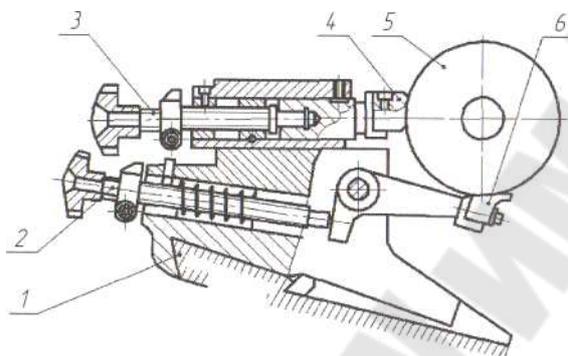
Люнет круглошлифовального станка: 1 – стол; 2,3 – винты; 4, 6 – башмаки; 5 – заготовка
